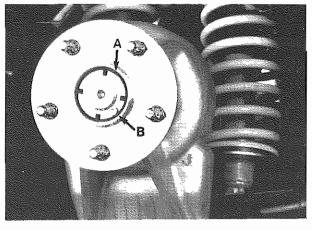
A - Vite a testa esagonale interna Socket head screw B - Ghiera fissaggio mozzo Hub ring nut
